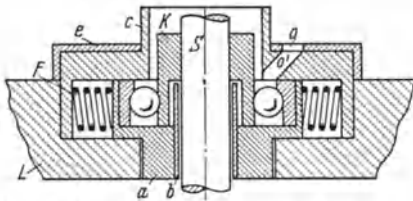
Halslager der Perfektspindel (Perfekt-Spindel A.-G., Windisch, Schweiz).
